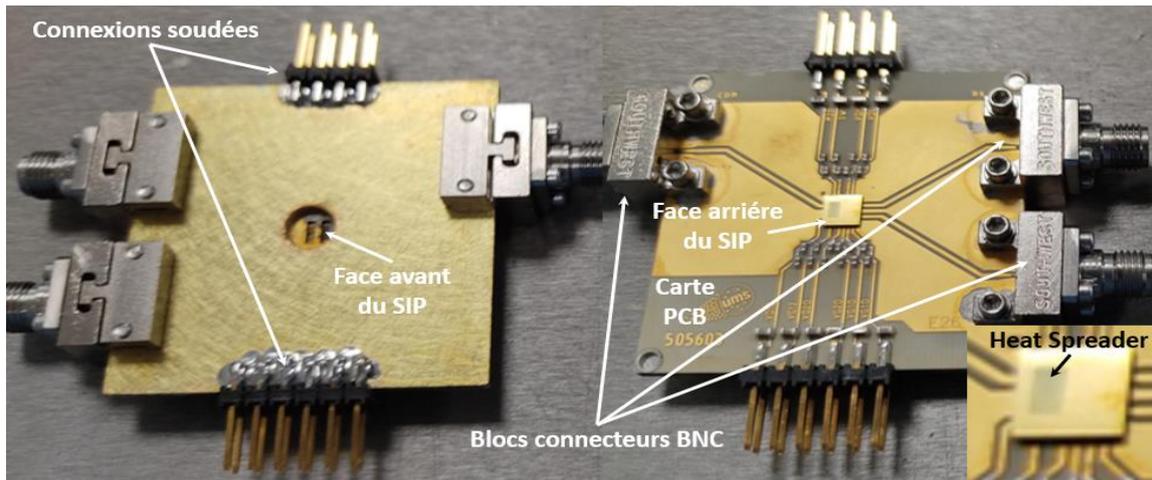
Démonstrateur télécom 5G assemblé sur PCB de la fonderie UMS, face arrière et face avant
